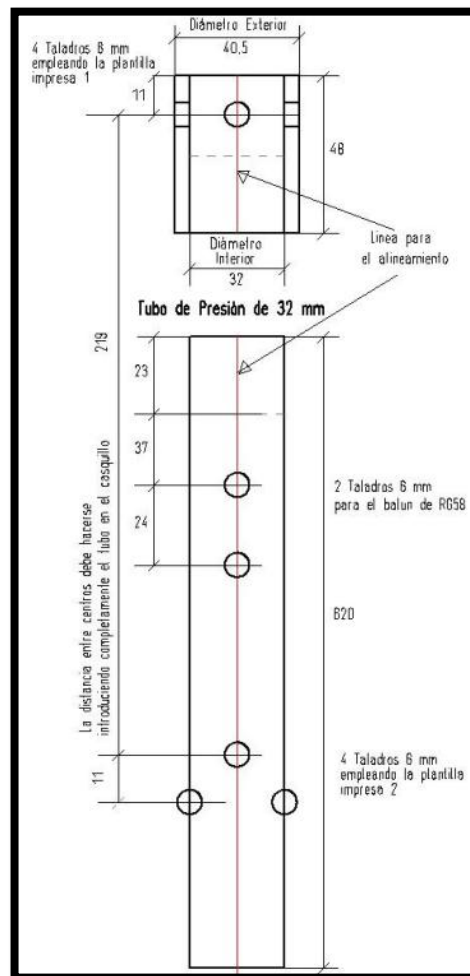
Plantilla de taladrado del tubo central de PVC
